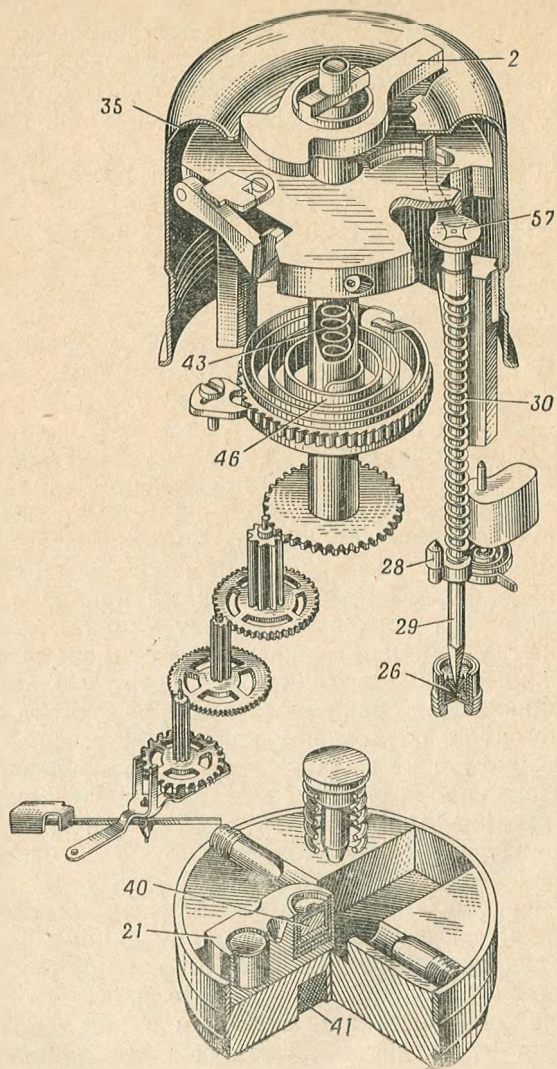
Схема расположения деталей при спуске дистанционного механизма:
